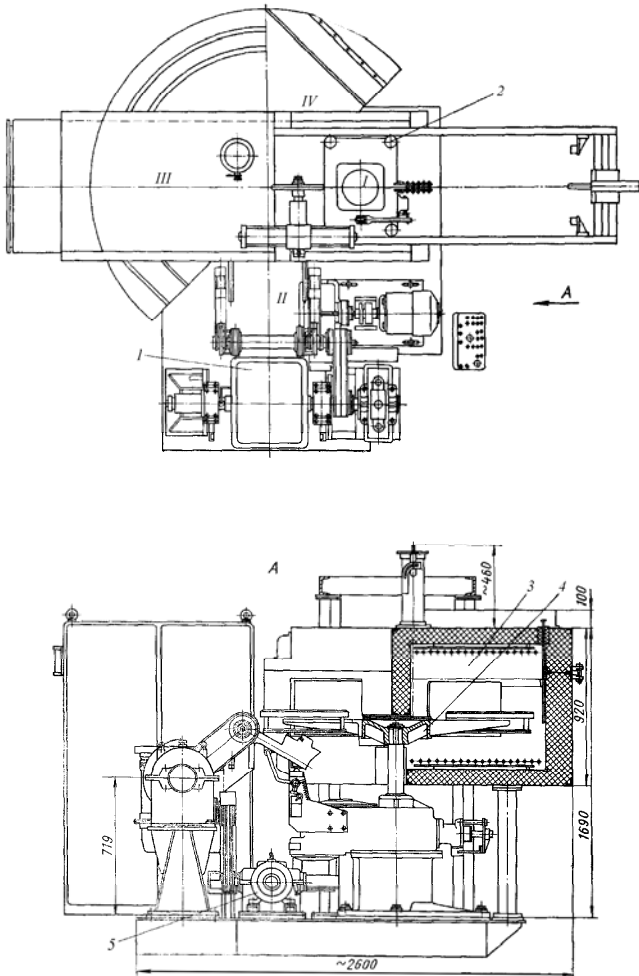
Чотирипозиційний автомат для виготовлення оболонкових півформ:
